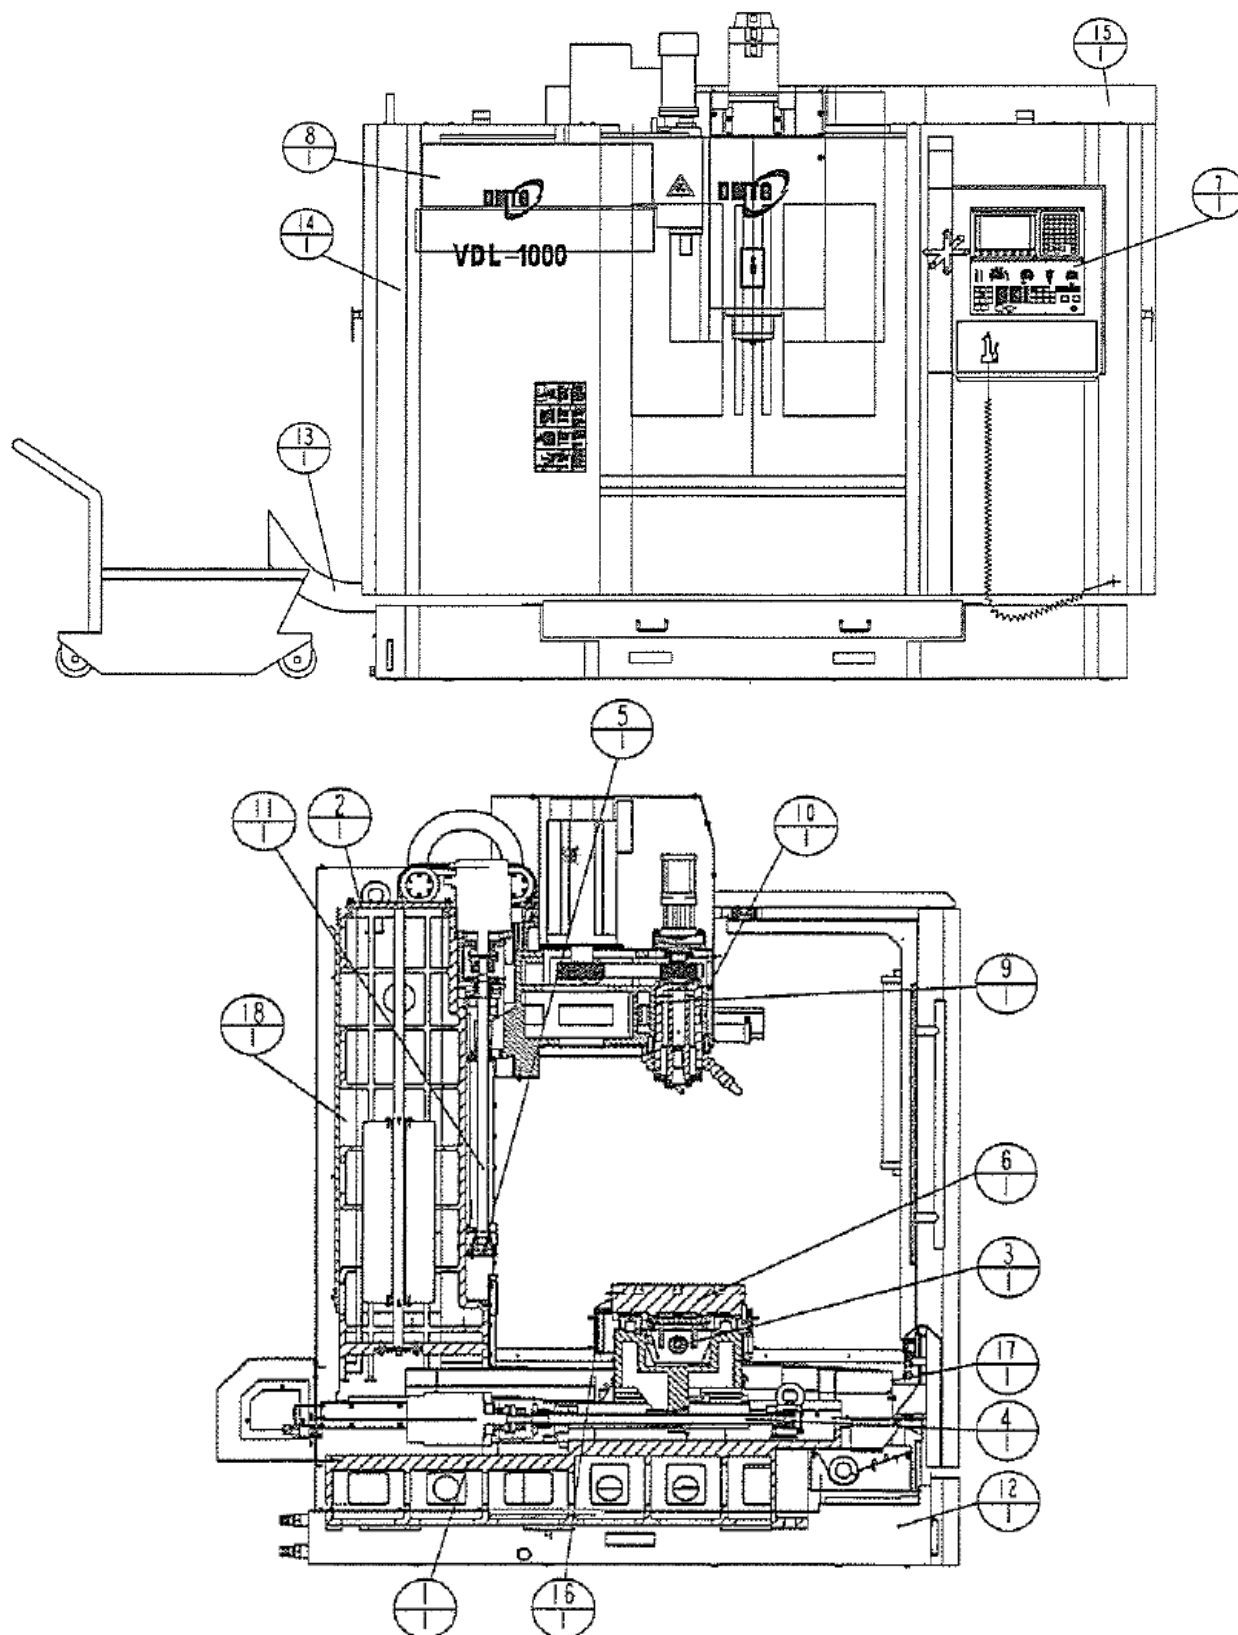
Расположение основных частей обрабатывающего центра VDL-800A
